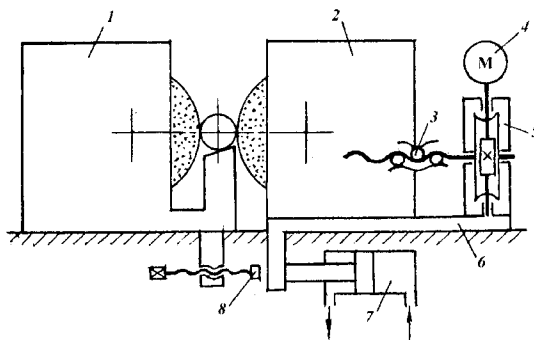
Принципова схема безцентрового круглошліфувального верстата з пристроєм мікропереміщень
